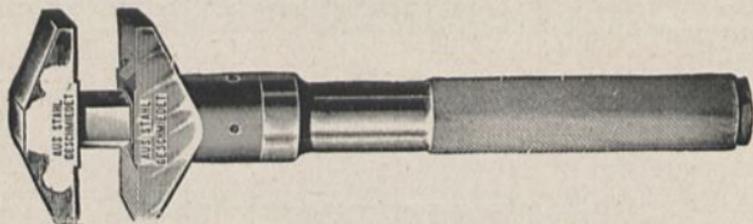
Verstellbarer Schraubenschlüssel (Engländer) der Firma H. Hommel, Mainz.
